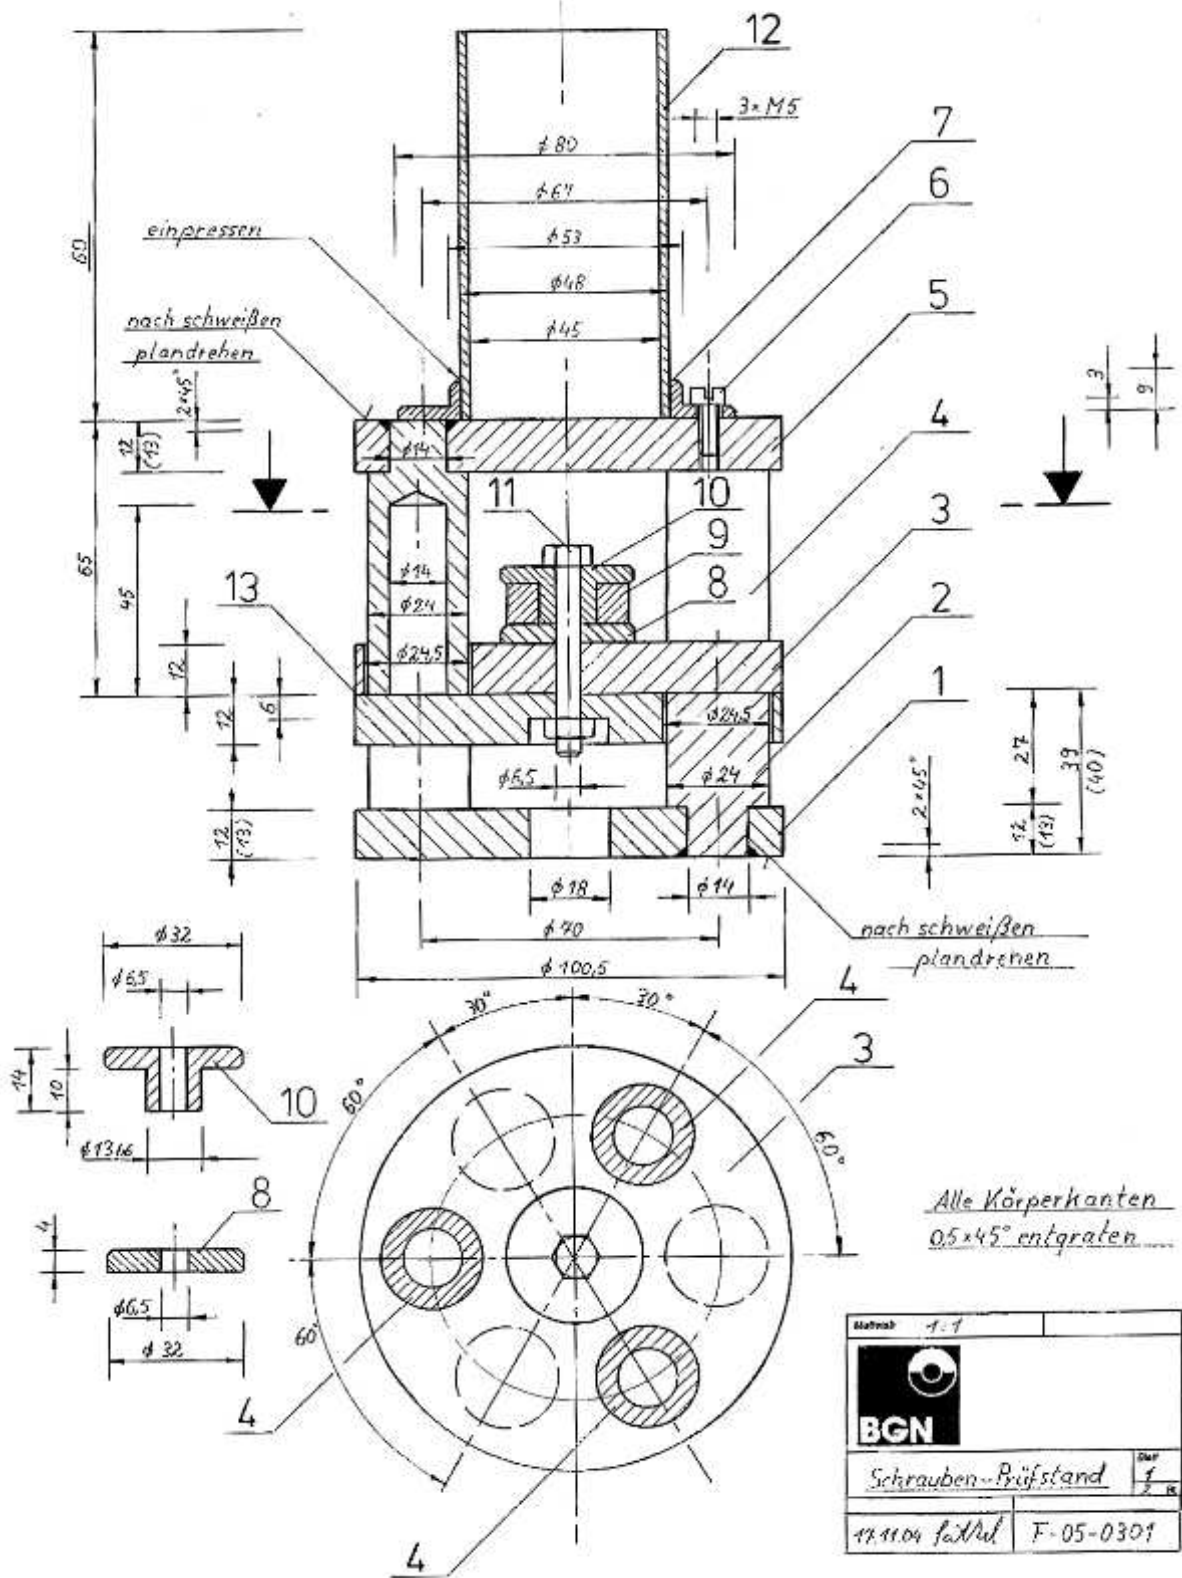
Blatt 1 der Konstruktionszeichnung für den Schrauben-Prüfstand.
